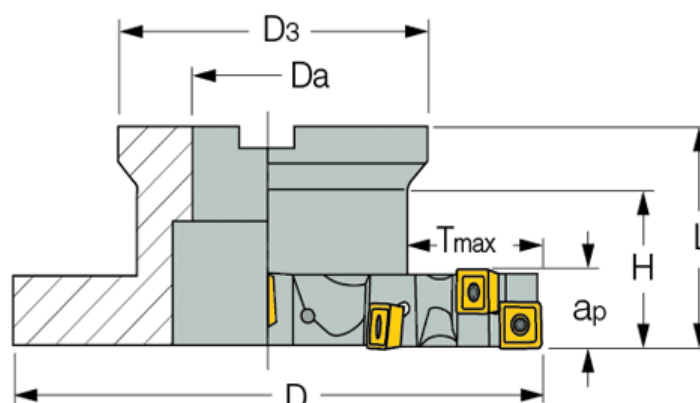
Дисковая фреза FDN D160-18-40-R12
